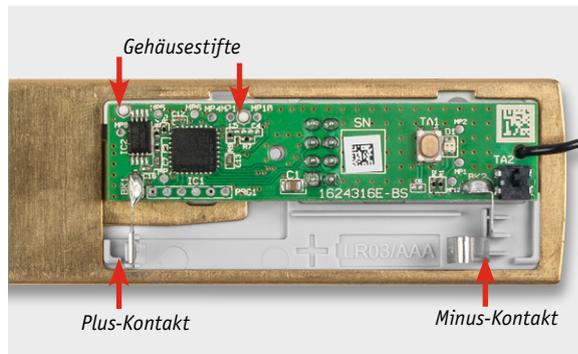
So liegt die Platine exakt im Gehäuse: Die Gehäusestifte ragen durch die Platine und die Batteriekontakte in den dafür vorgesehenen Halter.
